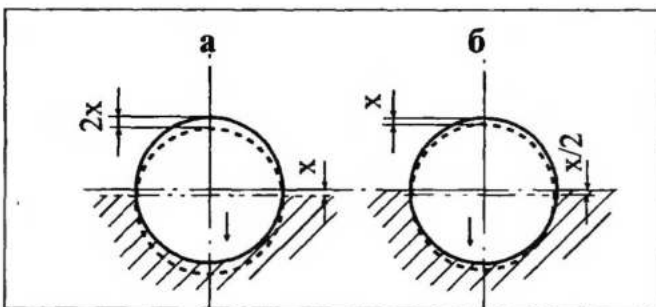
Схема смещения оси при ремонте разъемных отверстий (предполагается равномерный сьем металла при ремонте): а — поверхности разъема обработаны у основания и у крышки на величину X — смещение оси на величину X в сторону основания; б — поверхность разъема обработана на величину X только у крышки — смещение оси на X/2 в сторону основания; // — основание
